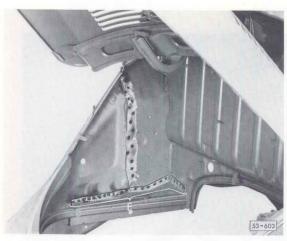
Seitenteil-Abschnittsteil, Motorabdeckblech und Abschlußblech hinten einschweißen.
